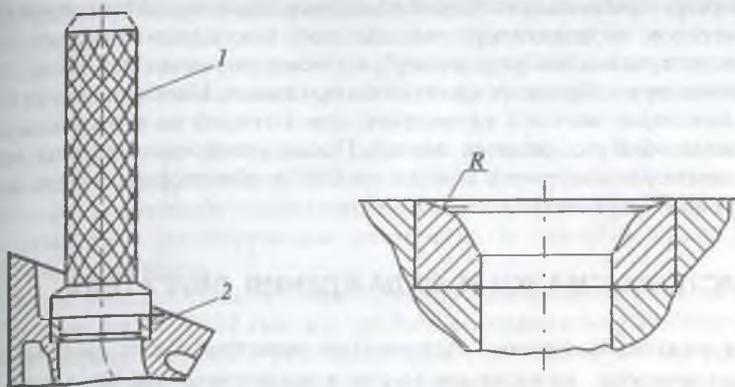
Запрессовка седла клапана (2) с помощью оправки (1)
